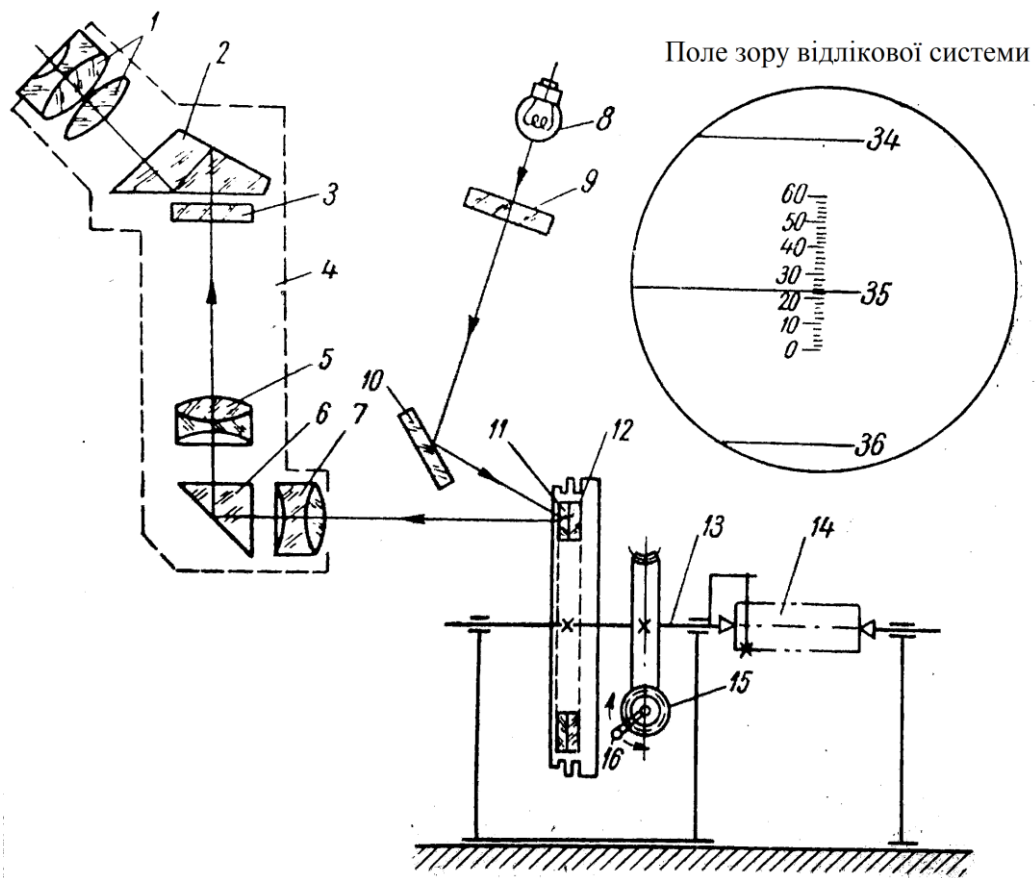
Принципова схема оптичної ділильної головки ОДГ-А
